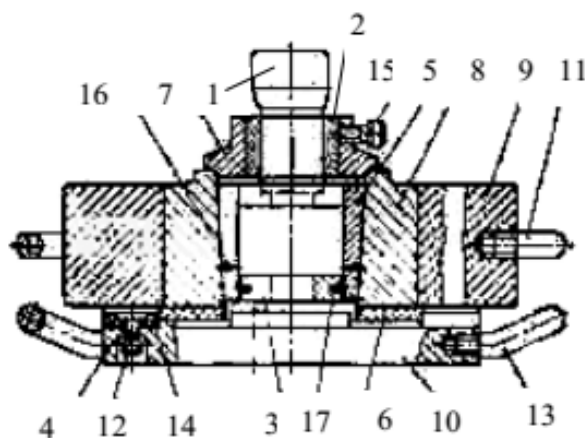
Универсальный пакет-штамп для холодного выдавливания:
